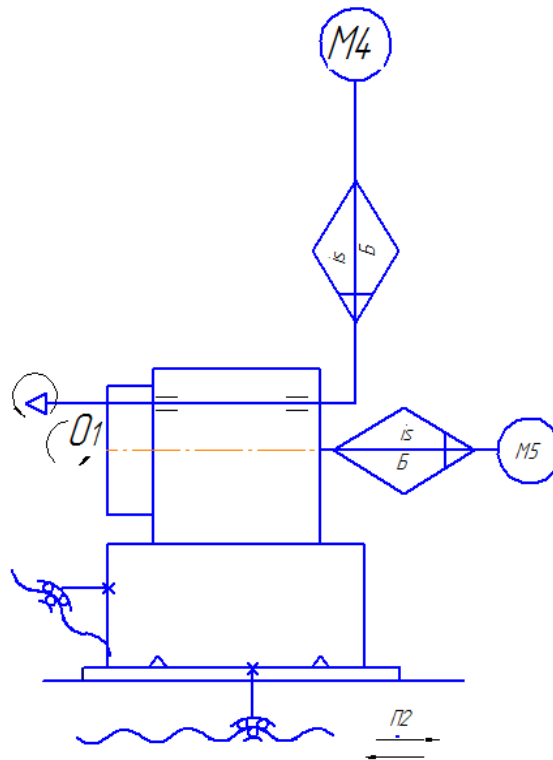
Ланцюг приводу обертового руху інструменту в револьверній головці
